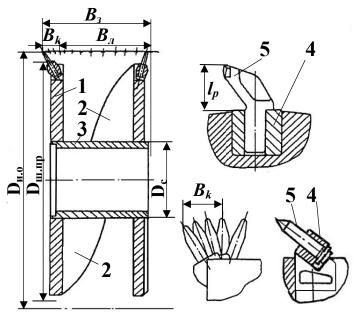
Шнек очистного комбайна: 1 — лобовина; 2 — погрузочная лопасть; 3 — ступица; 4 — резце-держатель; 5 — резец;  $l_p$  — вылет резца;  $B_s$  — ширина захвата;  $B_\pi$  — длина линейной части;  $B_\kappa$  — длина кутковой части шнека;  $D_{\text{и.о.}}$  — номинальный диаметр шнека;  $D_{\text{ш.пр}}$  — приведенный диаметр шнека;  $D_c$  — диаметр ступицы шнека
